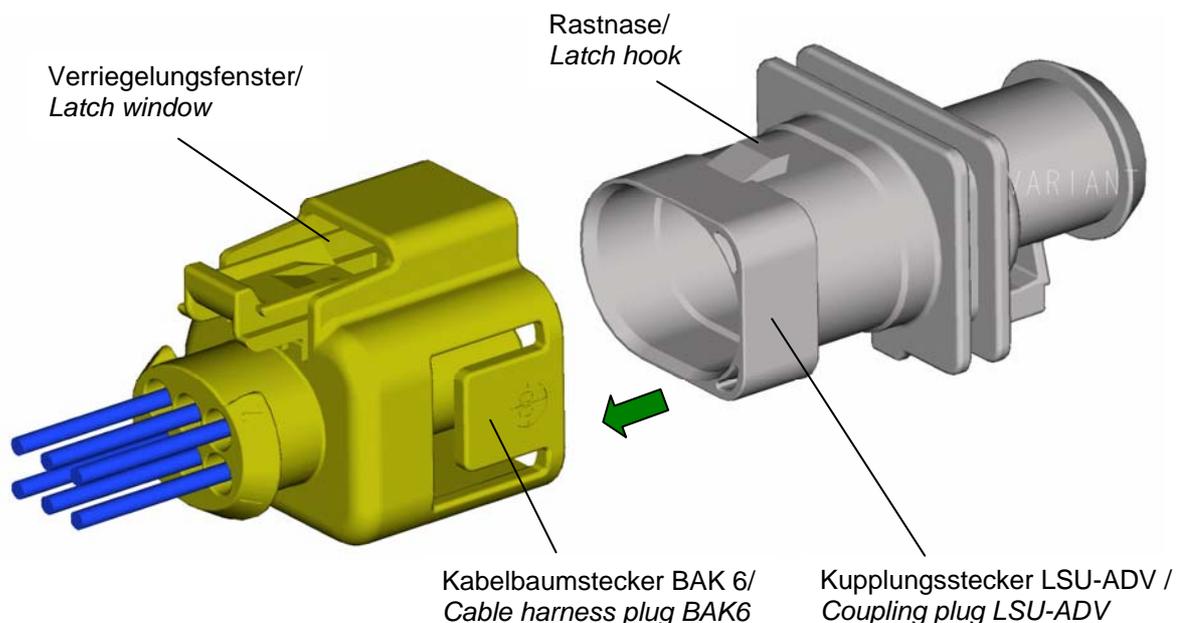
Montage Kabelbaumstecker mit Kupplungsstecker
